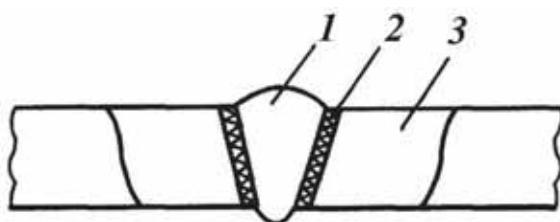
Схема строения сварного соединения: 1 – сварной шов; 2 – зона сплавления; 3 – зона термического влияния
